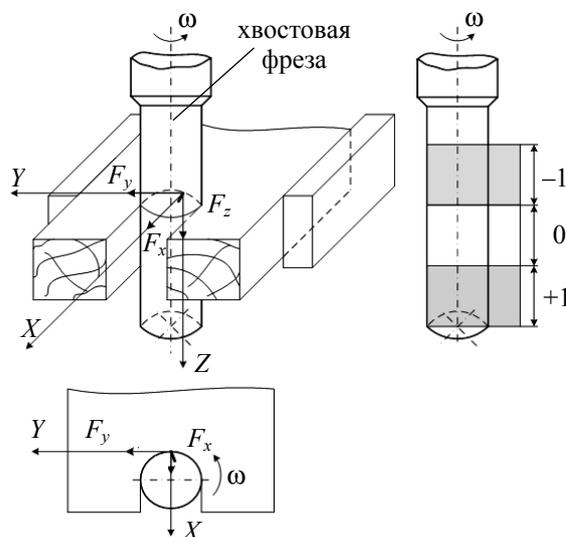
Схема обработки заготовок хвостовыми фрезами
